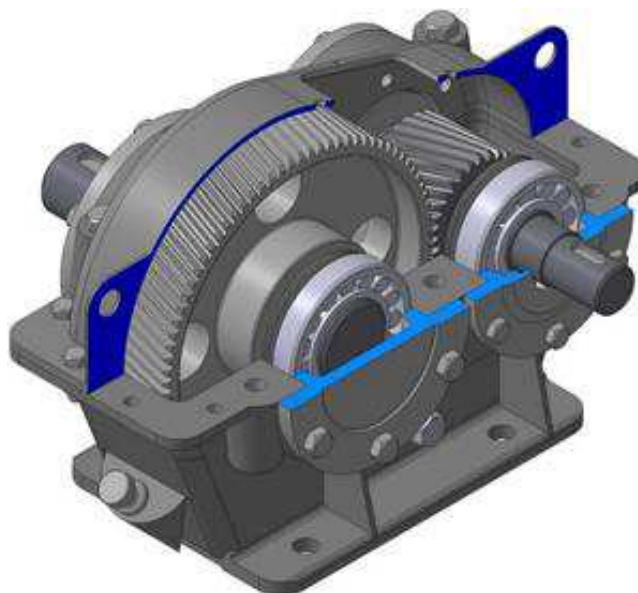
Цилиндрический редуктор с косозубым зацеплением колес
